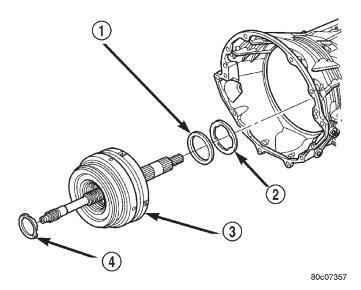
Desmontaje del conjunto de embragues de impulsión
